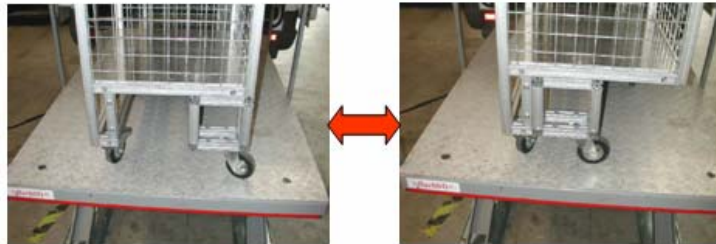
Gewählte Ausführungsvariante „Modulbefestigung“
